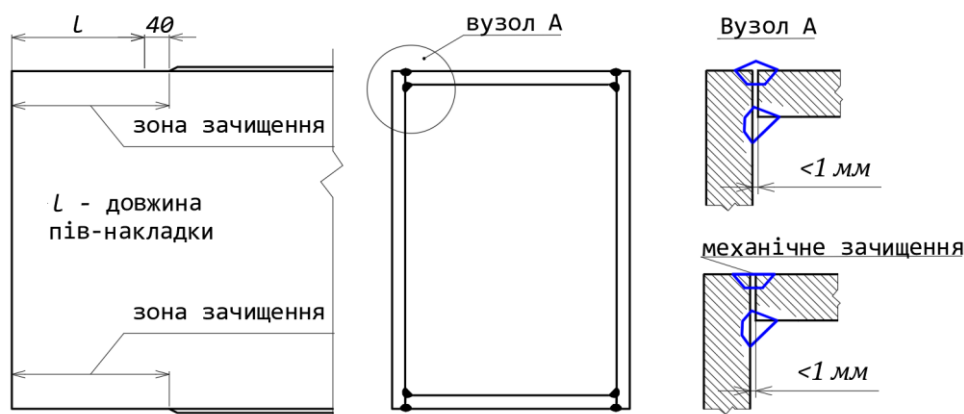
Схема обробки посилення шва зварювання коробчастого перерізу
